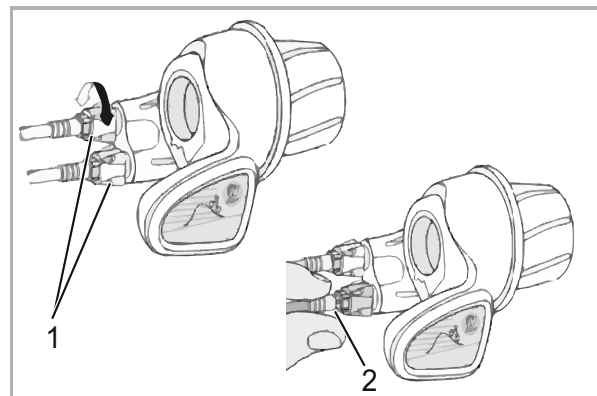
Slutmuffer (2) på to alternative udførelser (A og B) af et gearskifte med to kabler på baggaflen (1)
